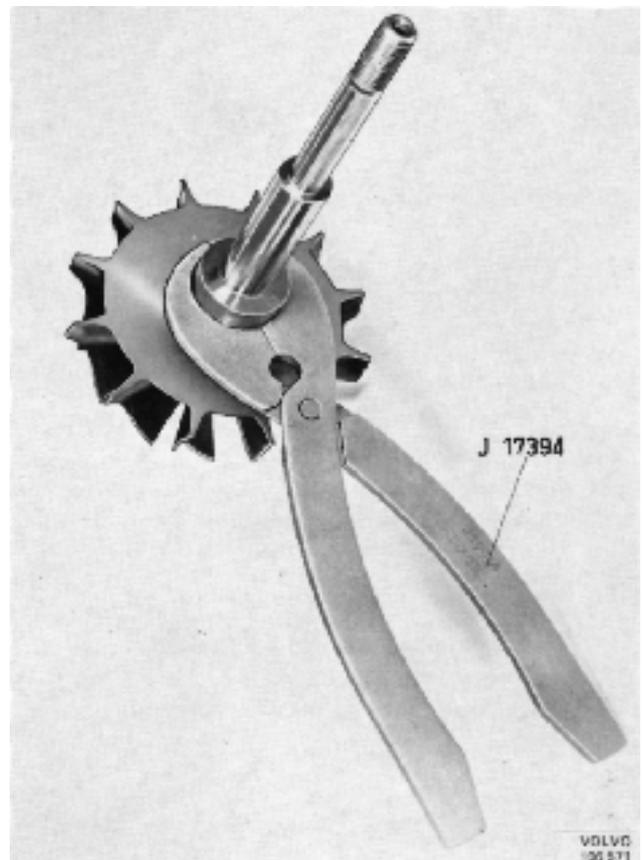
Holset J 17394 pour le montage de la roue de turbine avec l'arbre
